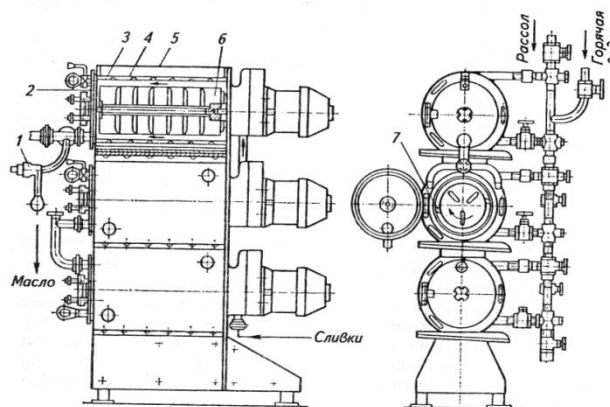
Цилиндрический маслообразователь: 1 – кран для выпуска масла; 2 – крышка; 3 – рабочий цилиндр; 4 – наружная обечайка; 5 – защитный кожух; 6 – вытеснительный барабан; 7 – ножи
